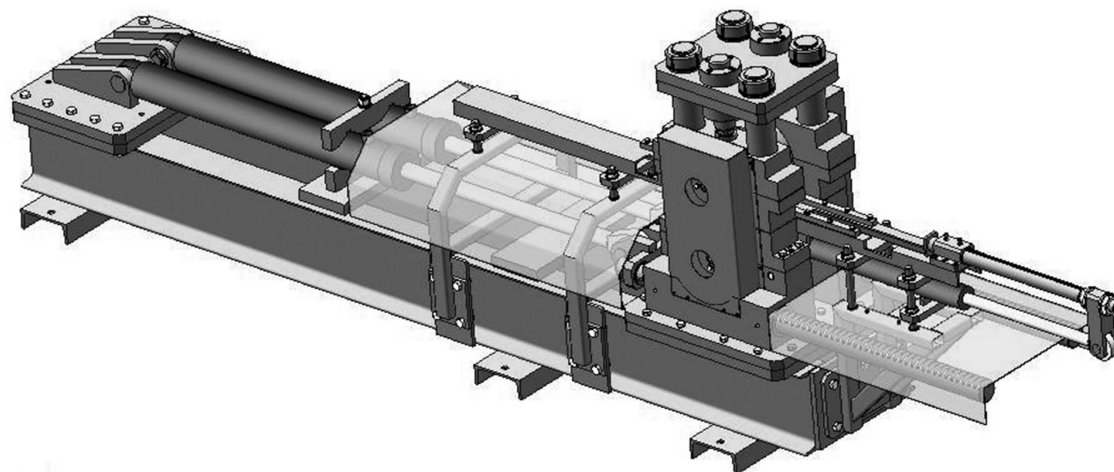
Прокатная установка для изготовления заготовок защитных элементов корпусов плугов
